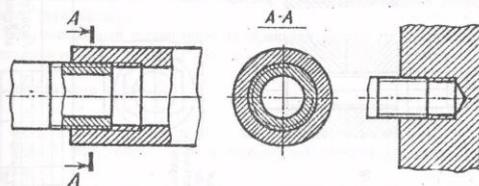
Изображение соединения двух деталей. Резьба на стержне "закрывает" резьбу в отверстии
